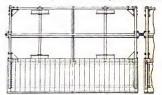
, Grundriss eines Wagens der Probebahn.
